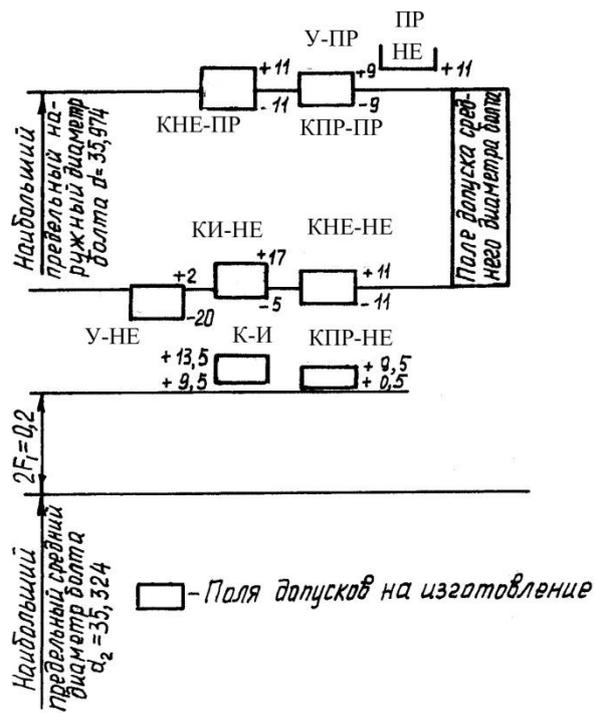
Схема расположения полей допусков наружного диаметра калибров для проверки болтов
